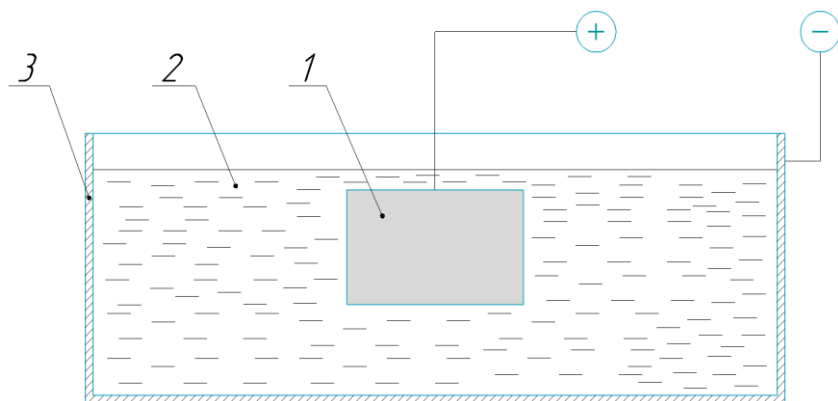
Принципиальная схема устройства установки для ЭПО:
